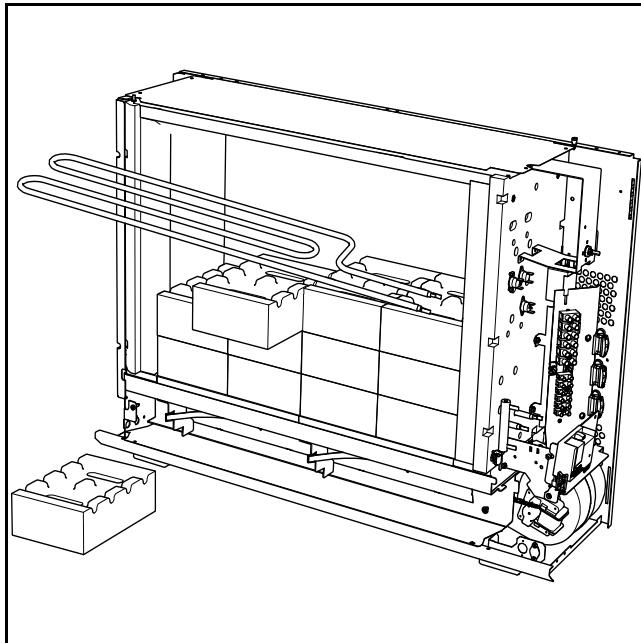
Posizionare la seconda e la terza fila di mattoni. Infilare il secondo elemento riscaldante.
